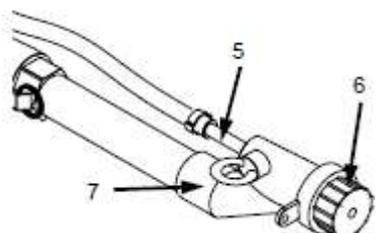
Трубка подачи воздуха к форсунке и форсунка для чистой штукатурки
